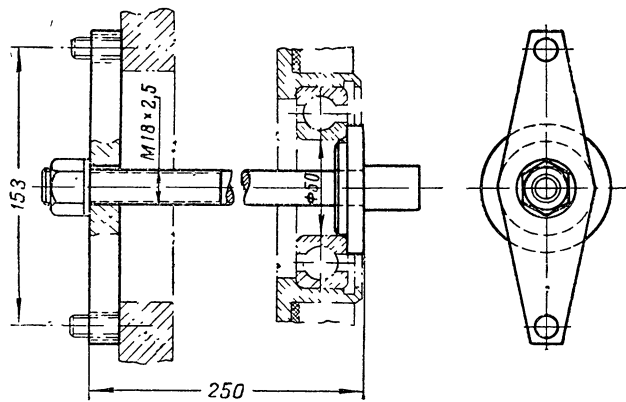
Приспособление для выпрессовки конуса переднего шарикоподшипника нижнего вала коробки передач.
